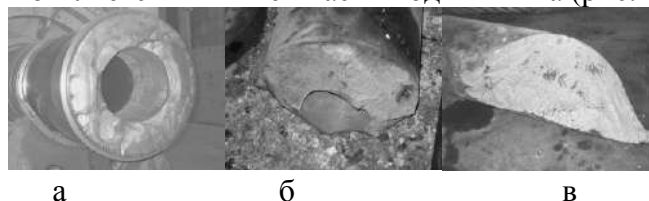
Разрушение валов: а – усталостный излом вала; б - разрушение вала из-за действия растягивающих сил в – «Косой» изгиб - вид излома при кручении и изгибе
